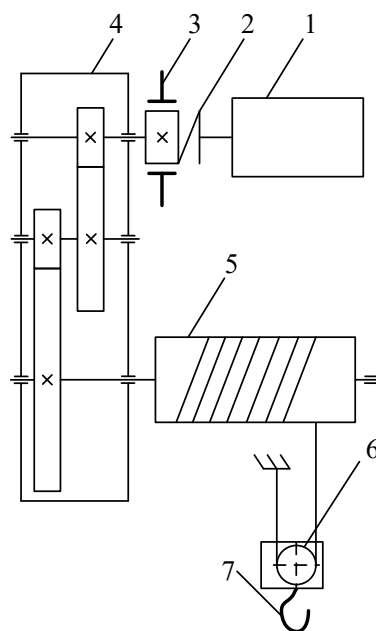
Кінематична схема підйомної лебідки: 1 – двигун; 2 – муфта; 3 – гальмо; 4 – механічна передача (редуктор); 5 – барабан; 6 – блок поліспасти; 7 – вантажозахватний пристрій
